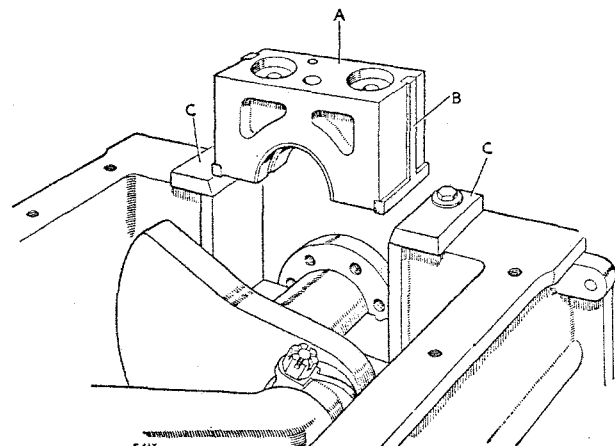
Montaje del sombrerete trasero y del conjunto de sellado.
